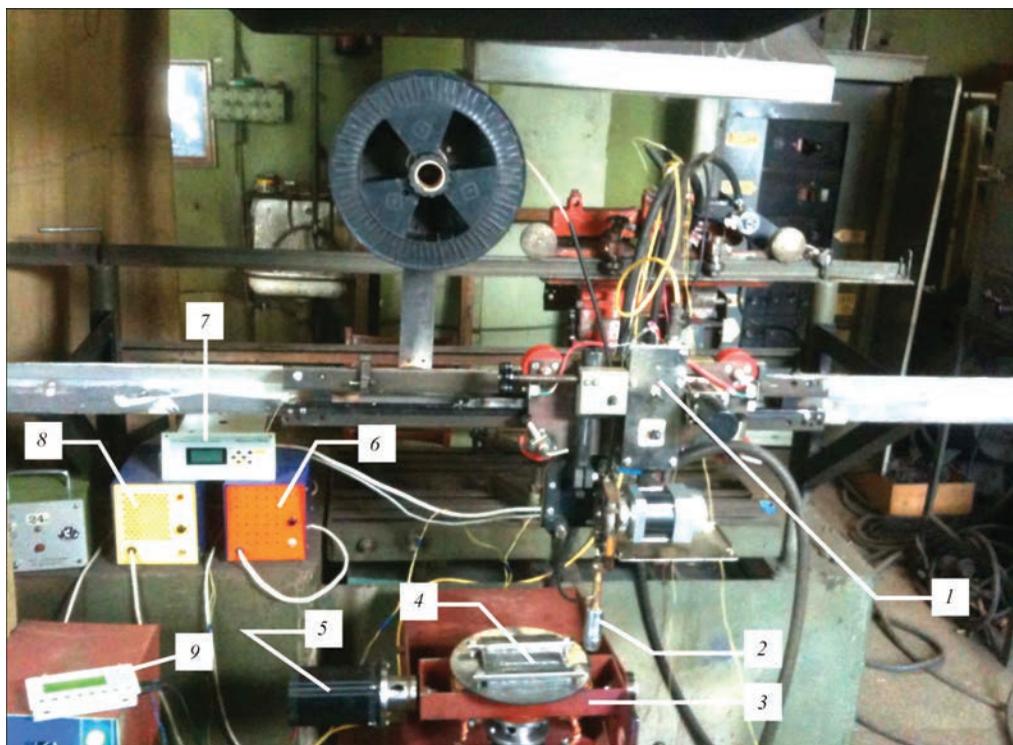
Схема установки для наплавки с подвижной станиной: 1 — пульт управления перемещения горелки; 2 — горелка; 3 — станина; 4 — наплавляемая деталь; 5 — двигатель, сообщающий колебания изделию; 6 — блок питания пульта управления поз. 1; 7 — индикатор скорости перемещения горелки; 8 — блок питания двигателя поз. 5; 9 — программируемый пульт управления режимом работы двигателя поз. 5
